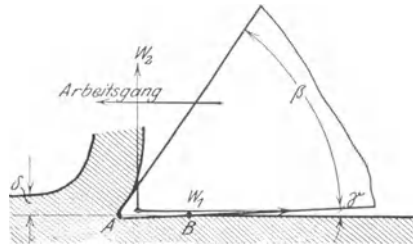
Schnittdruck bei einschneidigen Werkzeugen.
